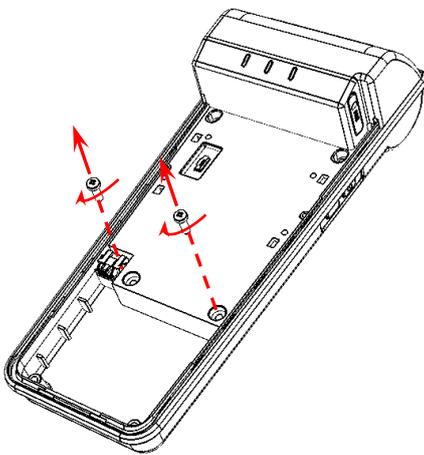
Демонтаж корпуса (открутить винты в верхней части корпуса)
